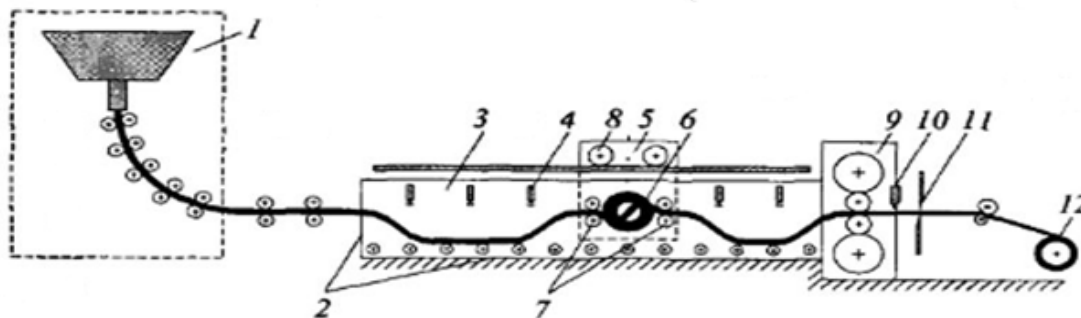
Ливарно-прокатний агрегат виробництва тонких сталевих смуг
